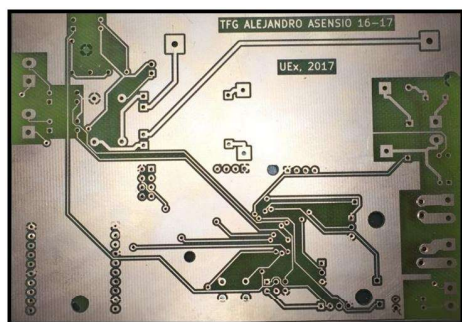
Imagen del PCB por lado de las soldaduras.
